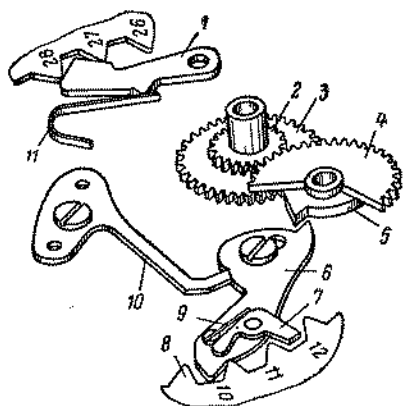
Кинематическая схема календарного устройства часов «Слава» 2414:
